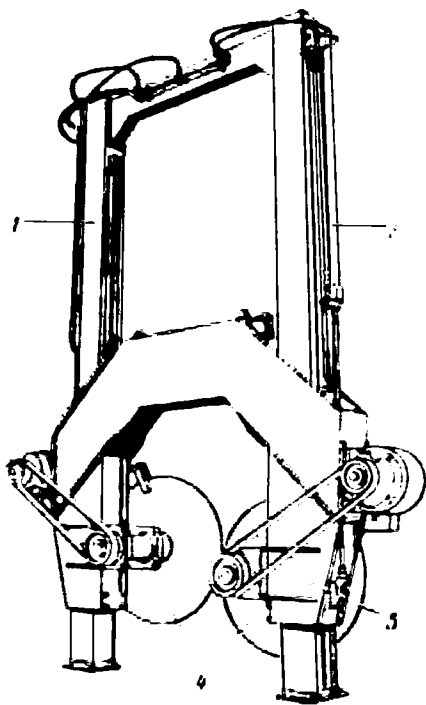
Общий вид станка со спаренными круглыми пилами:
